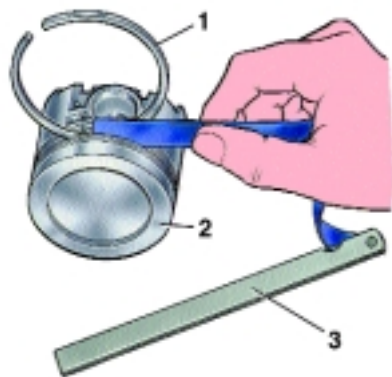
Проверка зазора между поршневыми кольцами и канавками: 1 – поршневое кольцо; 2 – поршень; 3 – набор щупов
